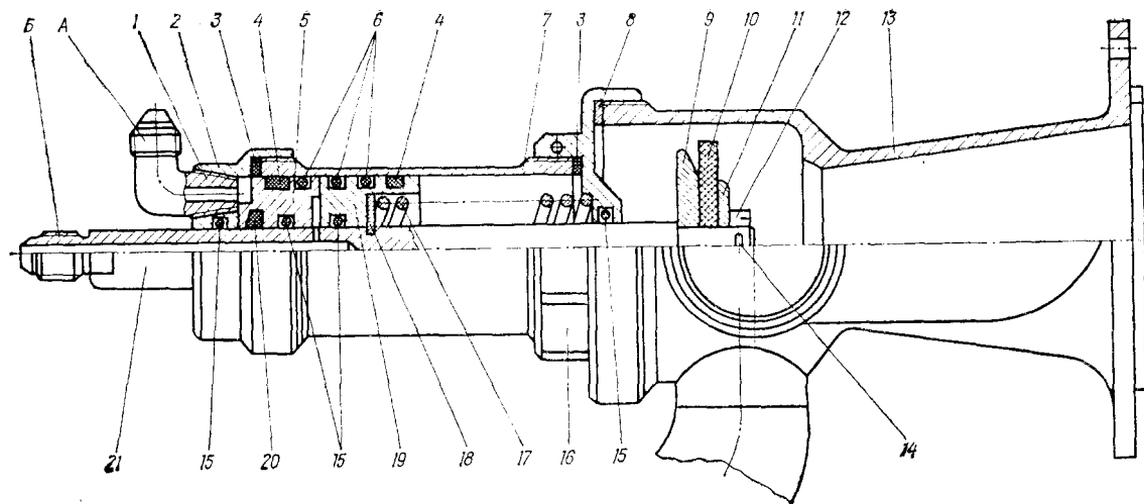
(ТК № 3.7). Пневмоклапан 2102.0272.160 в сборе с корпусом 2102.0272.170 (вып. 26): 1 — угольник ввертной 1-6-28-31А; 2 — крышка 2102.0253.118; 3 — кольцо паронитовое 2102.0272.169; 4 — кольцо войлочное 2102.0272.169—01; 5 — поршень 2102.0272.168; 6 — кольцо уплотнительное резиновое 2102.0272.164; 7 — цилиндр; 8 — кольцо уплотнительное паронитовое 2102.0272.108; 9 — прижим; 10 — прокладка резиновая 2102.0253.122—01; 11 — шайба; 12 — гайка М8; 13 — корпус 2102.0272.170; 14 — шплинт 2×20; 15 — кольцо уплотнительное резиновое 2102.0272.162—01; 16 — крышка 2102.0272.162; 17 — пружина; 18 — кольцо; 19 — поршень 2102.0272.172; 20 — кольцо войлочное 2102.0272.169—02; 21 — шток
